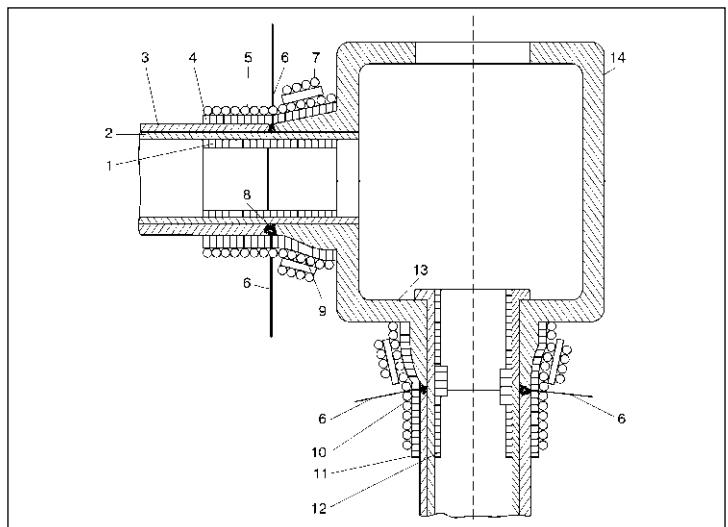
Общий вид сварных соединений приварки труб к патрубкам ГЦН на АЭС с реактором РБМК-1000: 1 — внутренняя теплоизоляция вертикального стыка; 2 — плакировка трубы и патрубка ГЦН; 3 — труба; 4 — наружная теплоизоляция вертикального стыка; 5 — первый слой (внутренний) индуктора; 6 — термоэлектрические термометры; 7 — второй слой (наружный) индуктора; 8 — горизонтальный сварной стык; 9 — асбосцементные прокладки; 10 — вертикальный сварной стык; 11 — наружная теплоизоляция горизонтального стыка; 12 — внутренняя изоляция горизонтального стыка; 13 — патрубок ГЦН; 14 — корпус ГЦН
